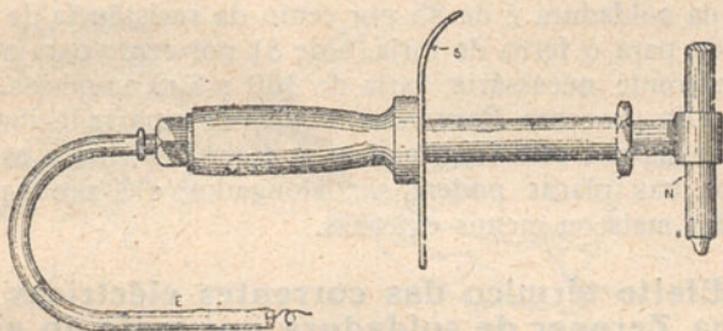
Máquina de soldar por arco, sistema Bernardos
